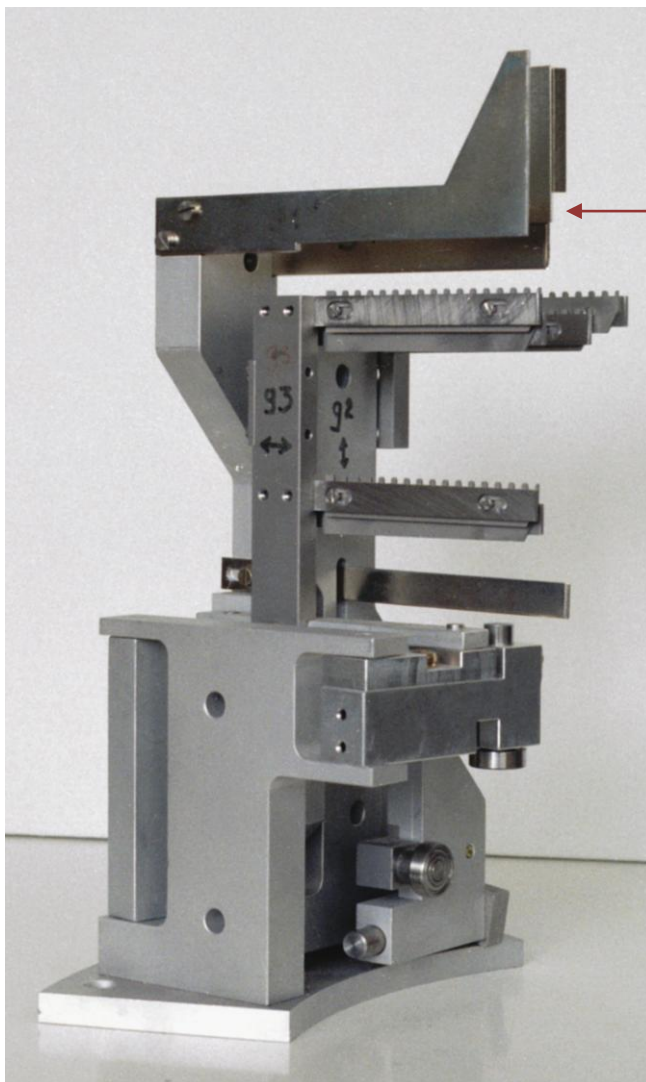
Helixturm, Rotorscheibe mit Steuerflächen für die Magazinbewegung, Detail der Nachbearbeitung, Foto: Achim Bunz
